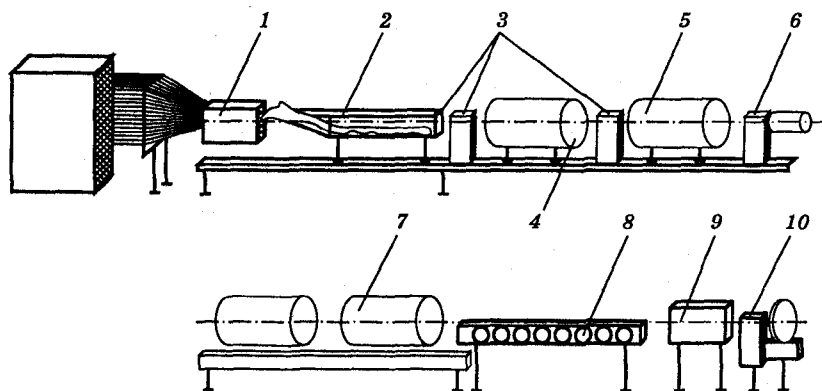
Схема изготовления пропитки волокнистых КМ с полимерной матрицей:
